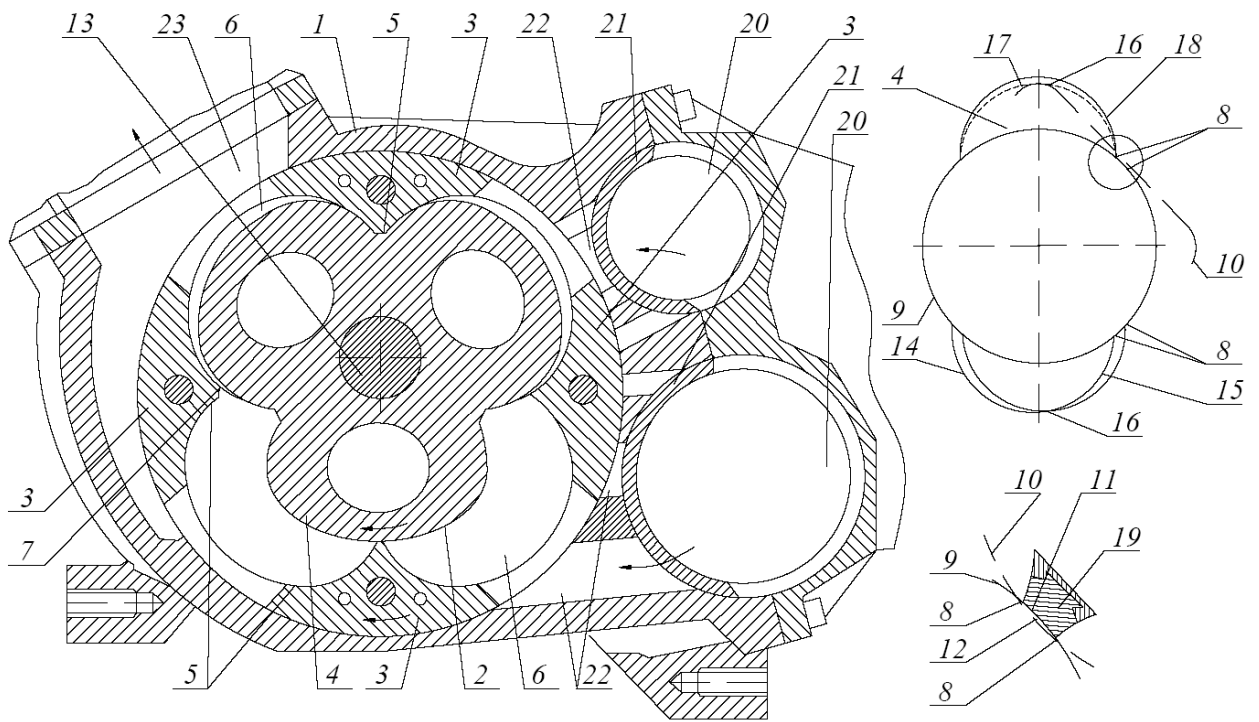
Роторно-поршнева машина з двома роторами [129]:
